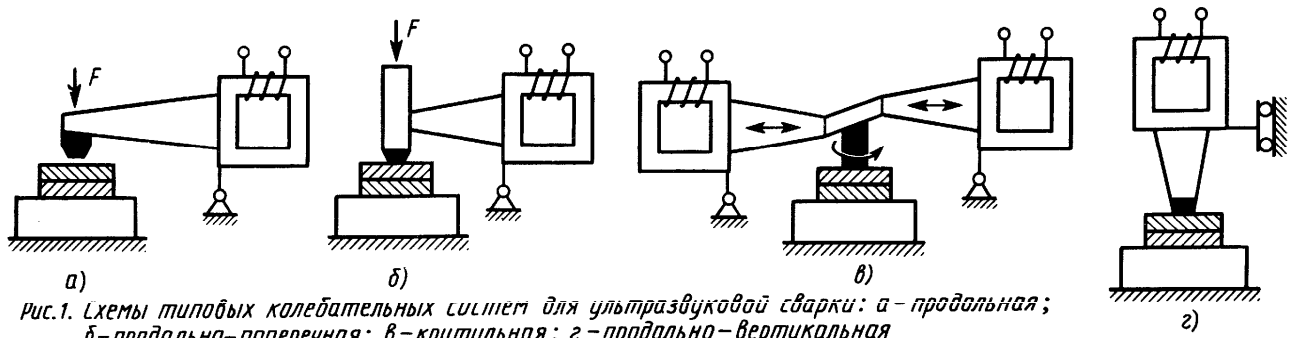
Схемы типовых колебательных систем для ультразвуковой сварки: а - продольная; б - продольно-поперечная; в - крутильная; г - продольно-вертикальная
